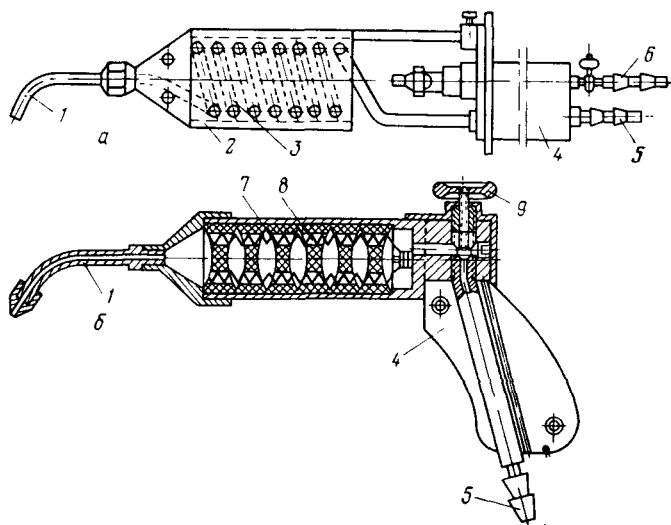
Сварочные пистолеты для сварки термопластов:
